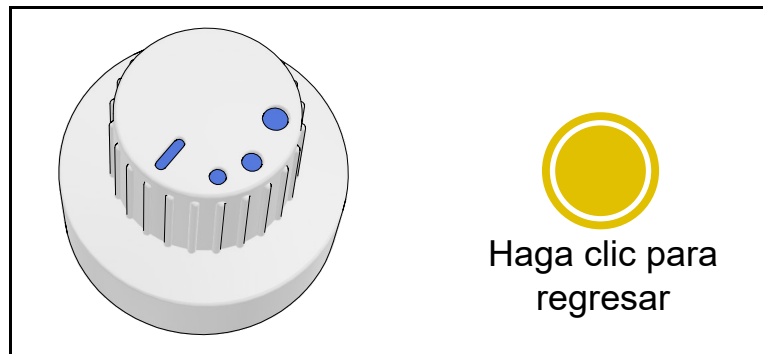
Selector de profundidad de la cuchilla 8067050
